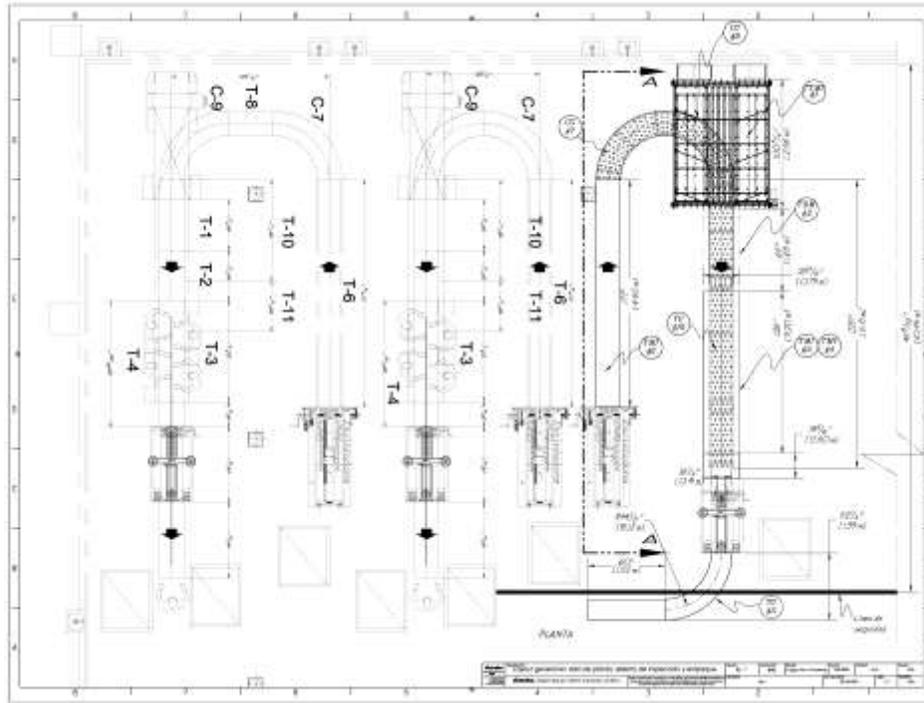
Layout del proyecto en vista de planta (fuente: desarrollo propio).
